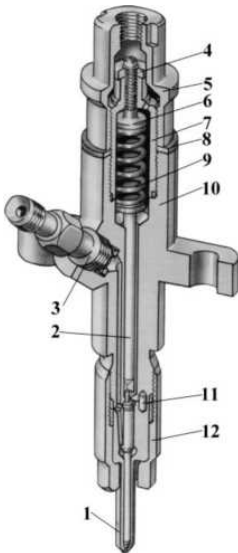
Устройство форсунки: 1 - распылитель; 2 - штанга; 3 - штуцер подвода топлива; 4- контргайка; 5 -колпак форсунки; 6 - регулировочный винт; 7 - гайка пружины; 8 - прокладка; 9 - пружина; 10 - корпус форсунки; 11 -штифты; 12 - гайка распылителя.
